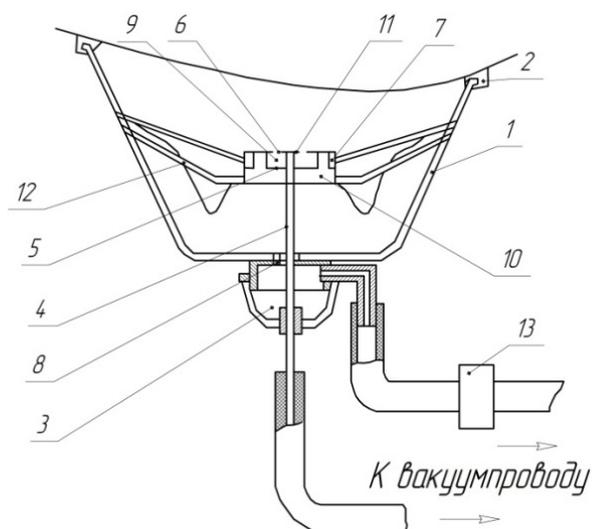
Схема устройства для массажа вымени животных, выполненного по варианту В-3: 1 – кожух; 2 – уплотняющий элемент; 3 – пневмокамера; 4 – шток; 5 – рабочий орган; 6, 7 – отверстия; 8, 11 – калиброванные отверстия; 9, 10 – камеры рабочего органа; 12 – гибкие элементы; 13 – пульсатор
